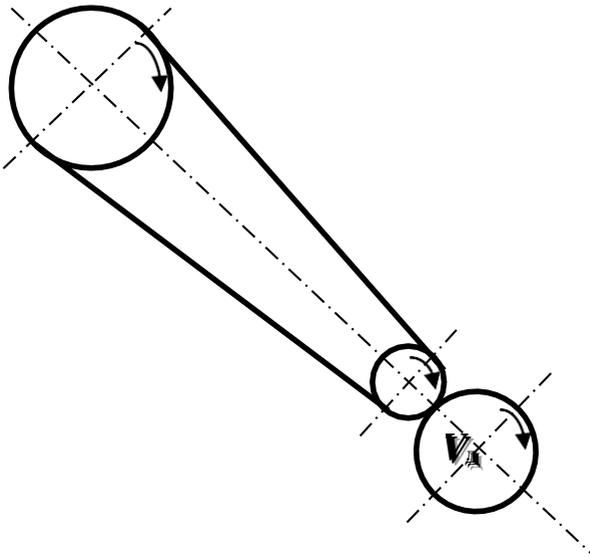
Схема обробки рухомою стрічкою з контактним роликком
